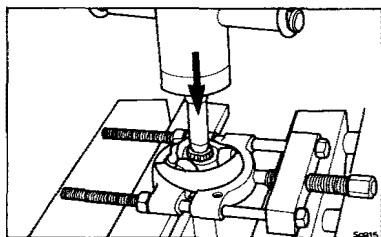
Снятие крестовины с вала привода с помощью пресса
